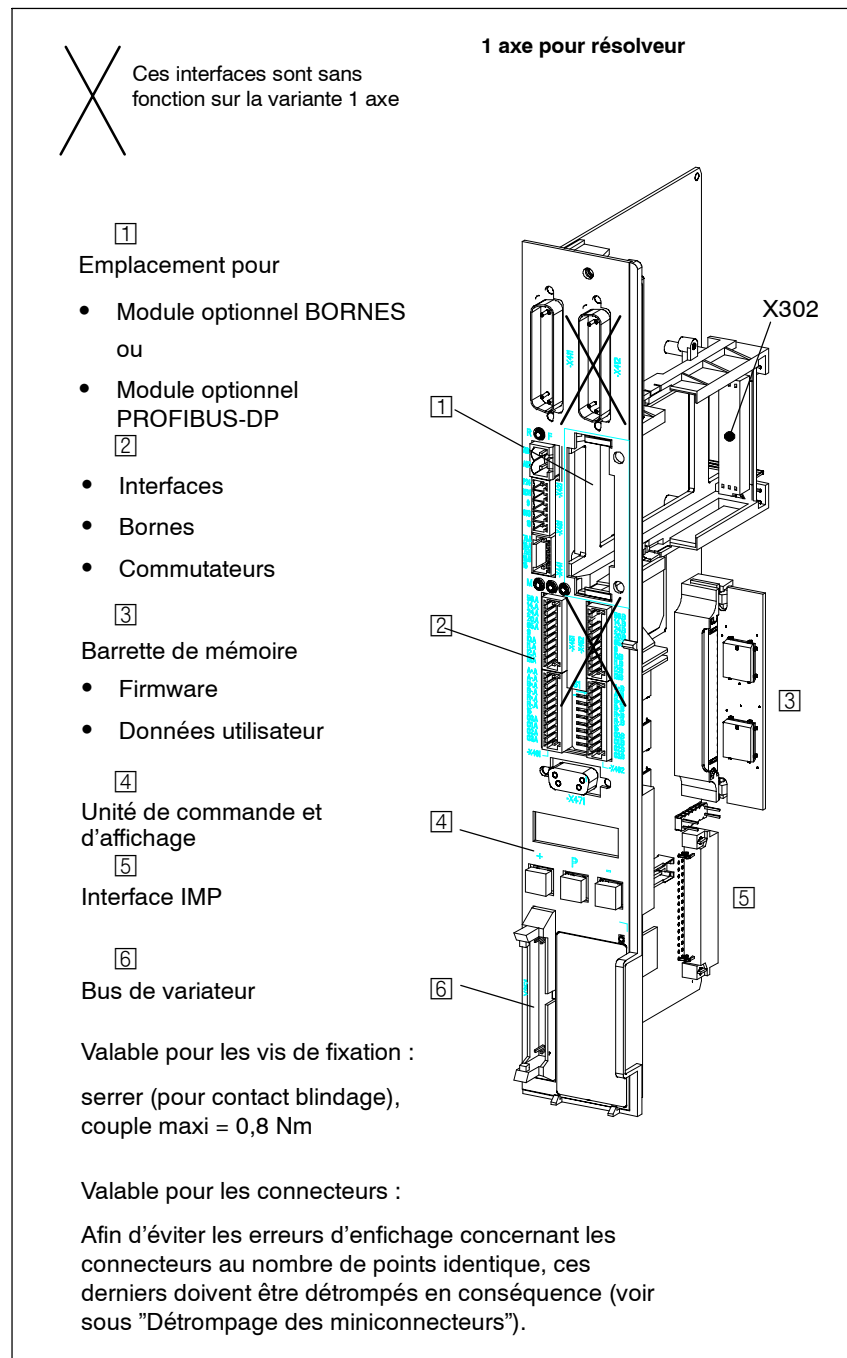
Carte de régulation pour 1 axe (SIMODRIVE 611 universal HRS)
